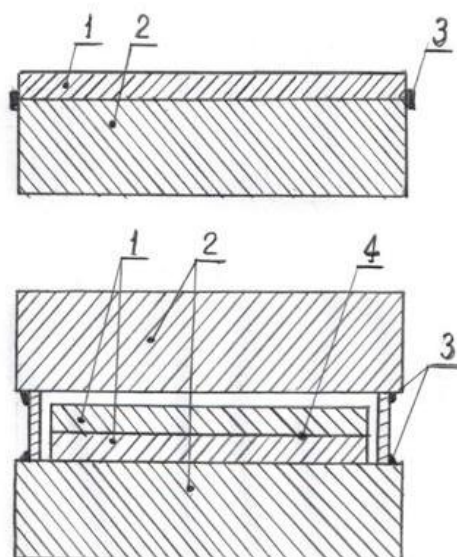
Конструкции пакетов для сварки прокаткой:
